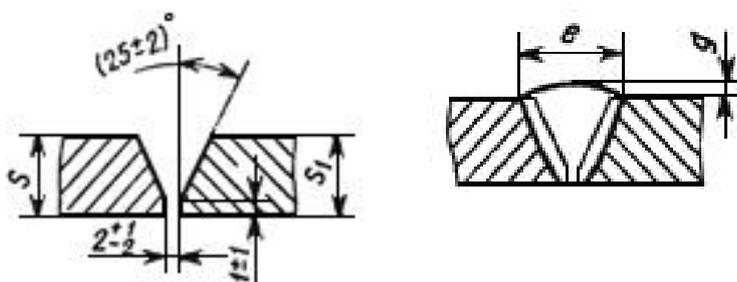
Конструктивные элементы разделки и сварного соединения:
